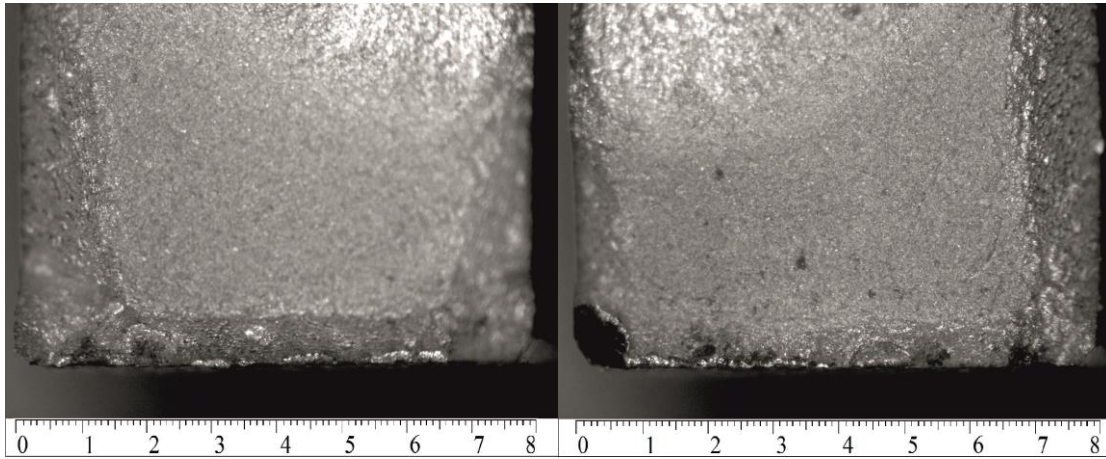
Grietas de 2 probetas con shot peening y combinación 8
